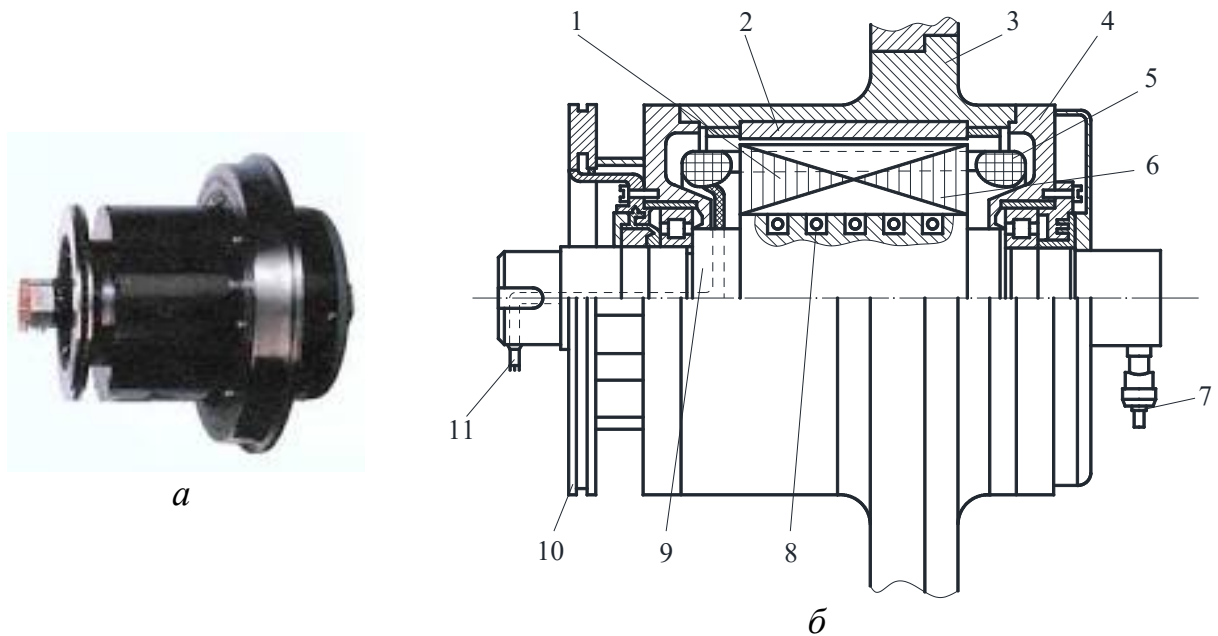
Загальний вид (а) і конструктивна схема (б) асинхронного двигуна з зовнішнім ротором для приводу колес електротранспорту:
